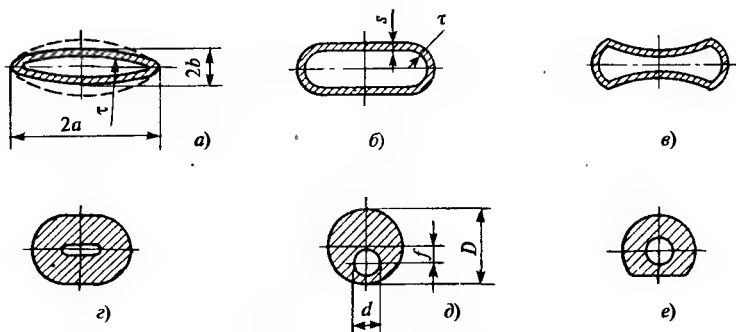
Формы сечения одновитковой трубчатой пружины:
